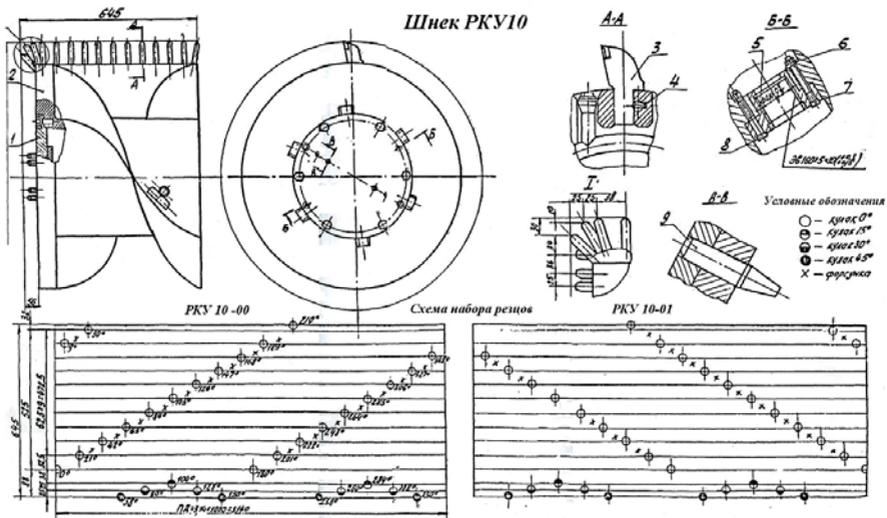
Шнековый исполнительный орган комбайна типа РКУ10. 1 - крышка; 2 - шнек сварной; 3 - резец ЗР4.80; 4 - стопор ПБК001; 5 - ступица; 6 - гайка М30.6 СТП21-79; 7 - болт КШЗМ.43; 8 - штифт; 9 - зубок ШБМ2С-1-1-04.
